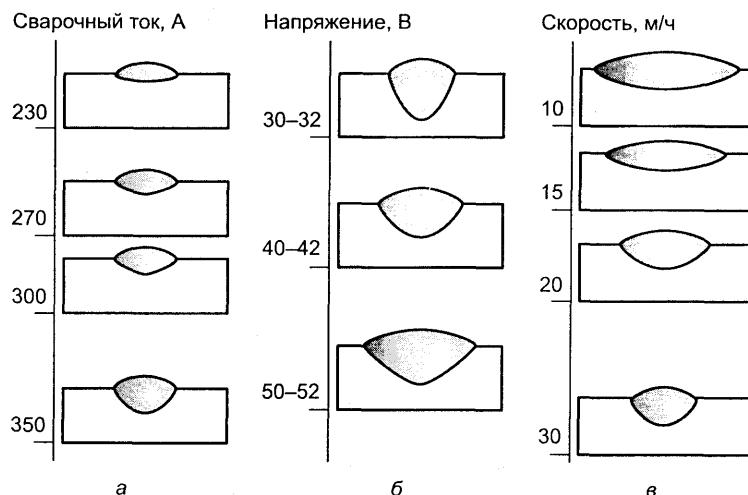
Влияние на форму и размеры шва сварочного тока (а), напряжения дуги (б), скорости сварки (в)
